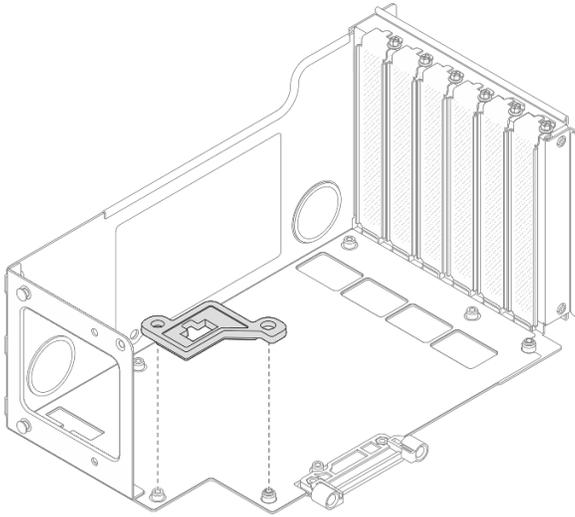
Installation du guide de connecteur sur le boîtier de carte mezzanine
